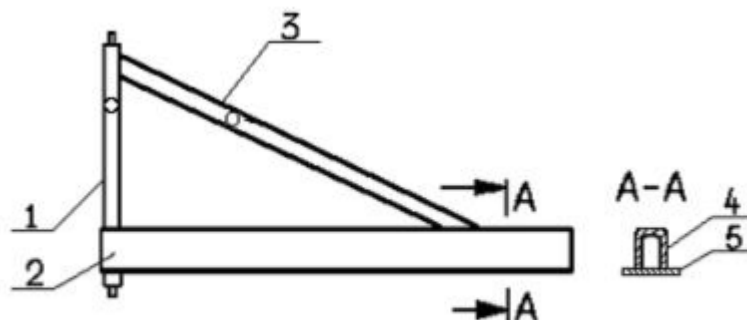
колонна (труба); 2 – стрела балочного типа; 3 – оттяжка (труба); 4 – гнутый П-образный профиль; 5 – нижний пояс балки (лист, полоса).
